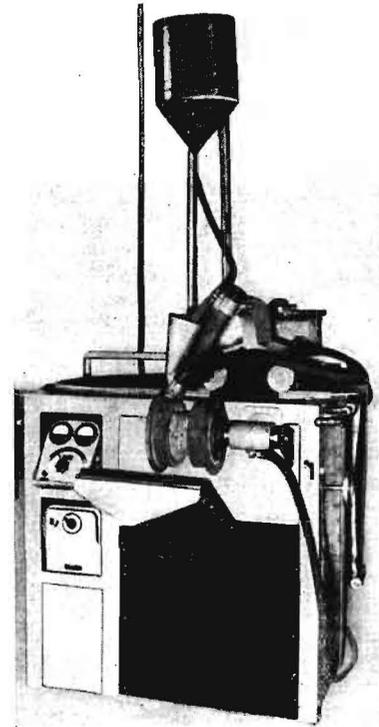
Laufrolle für KS 07/62, auf Automaten (Bild 1) aufgeschweißt
